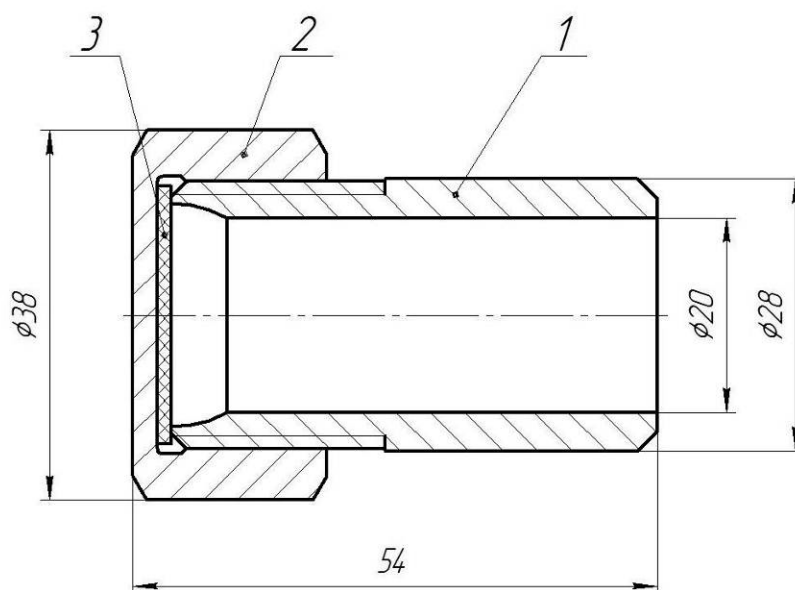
Устройство для опрессовки и продувки УОП-32
